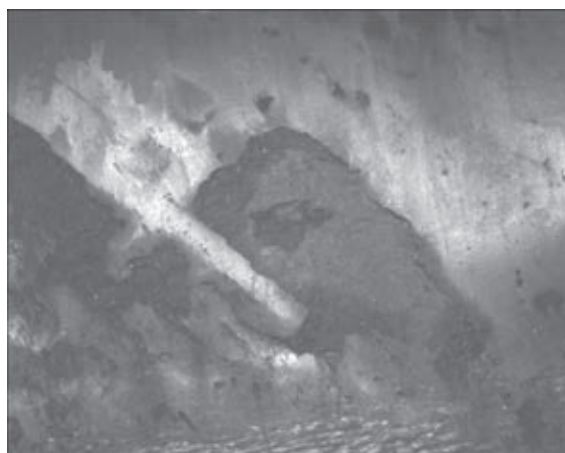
Вид повреждений металла облицовки КРК из стали СтЗсп
